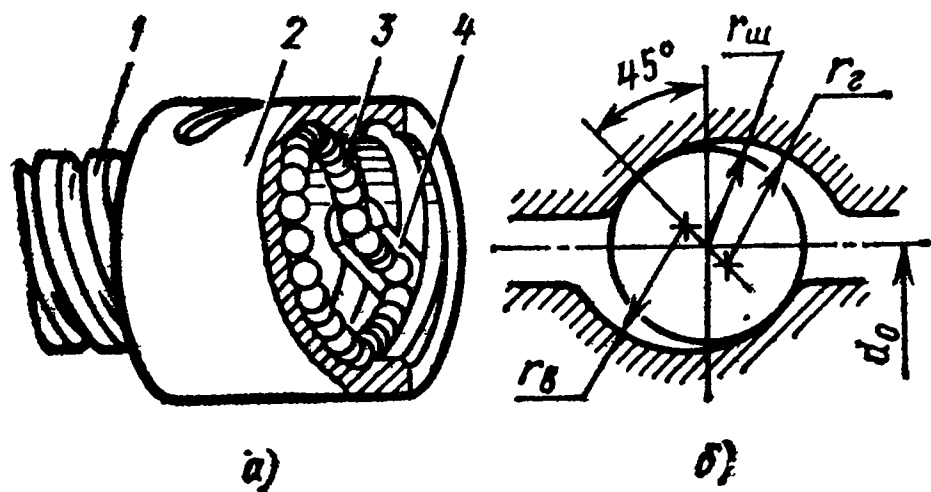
Передача винт—гайка качения (а) и полукруглый профиль резьбы (б)
